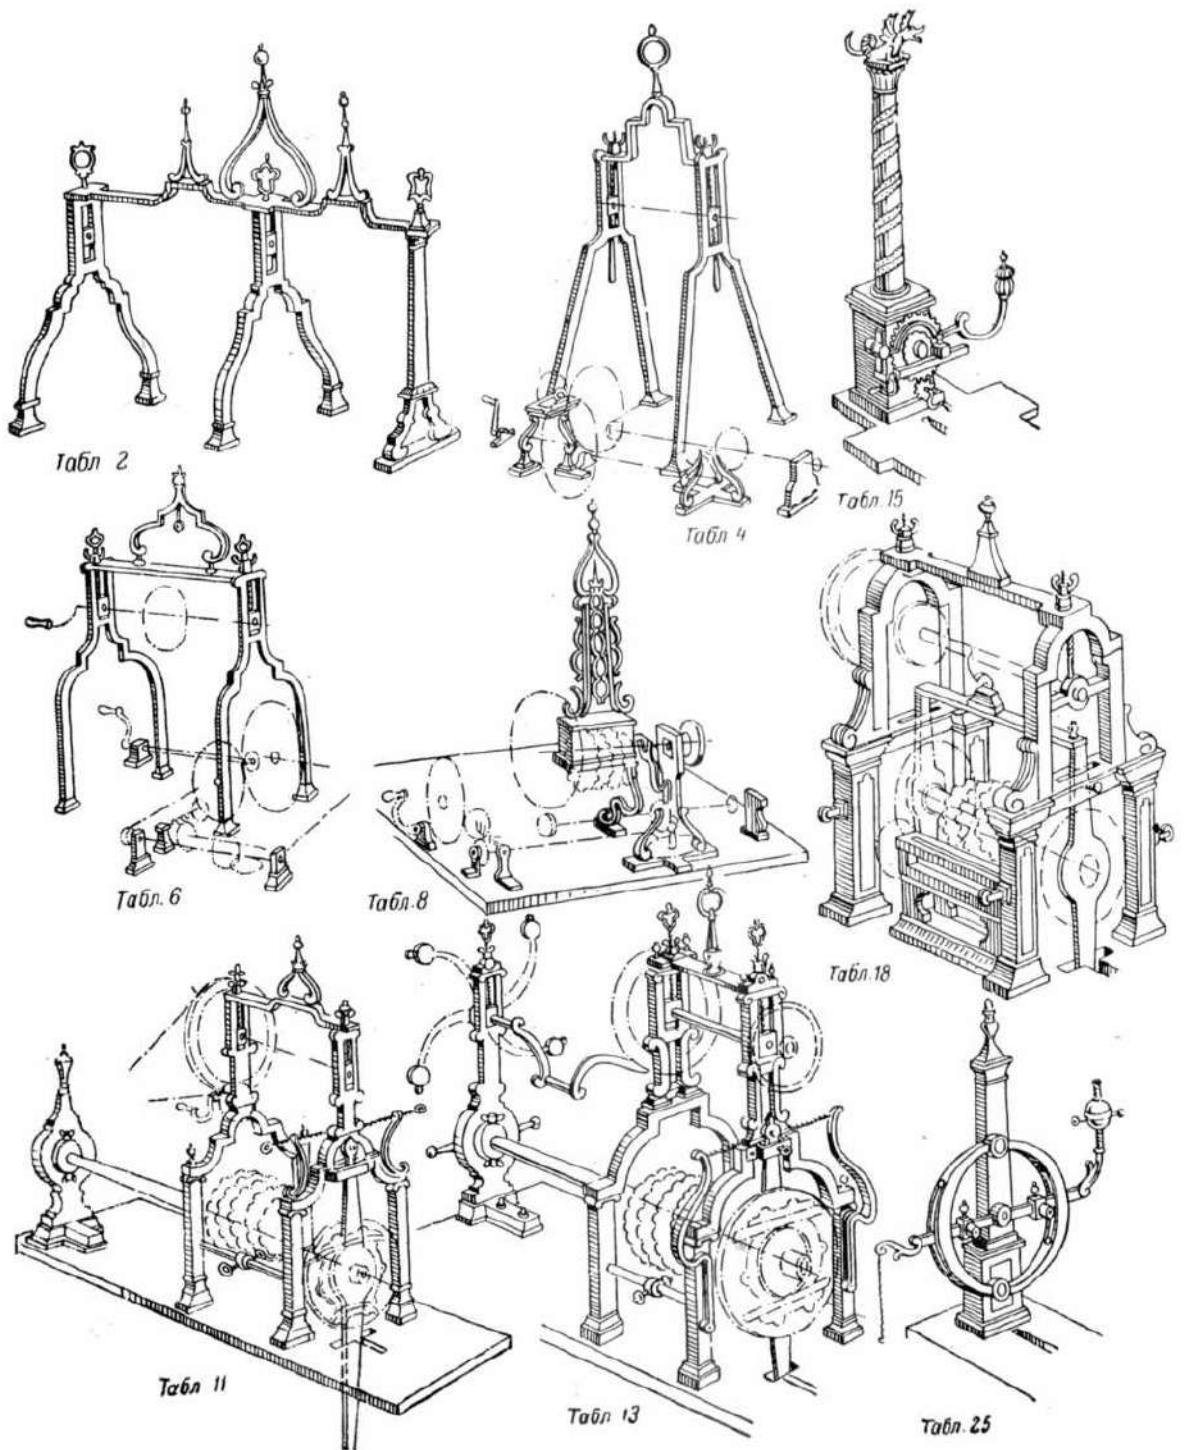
Конструкции копров — металлических верхних опор передачи в станках,
